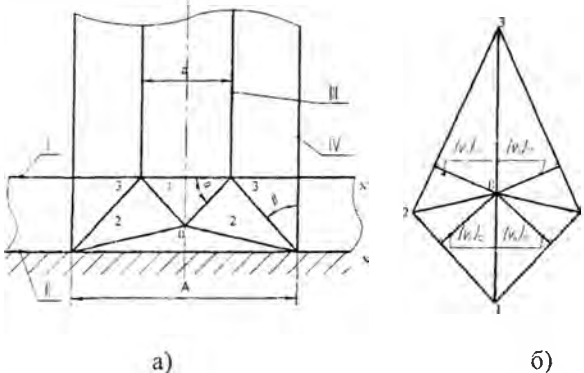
Кинематически возможное поле линий скольжения, принятое для теоретического анализа процесса РСО: а - поле линий скольжения; б - годограф скоростей; I – слой коррозии, II – обрабатываемая деталь, III – струя, IV – корпус
